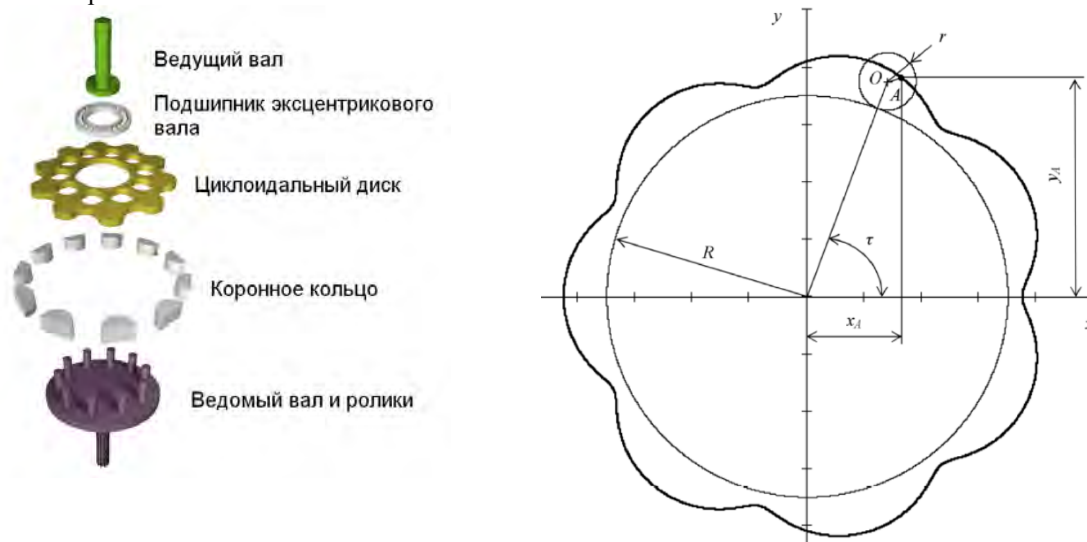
Общая схема компоновки цевочного редуктора и геометрический профиль
